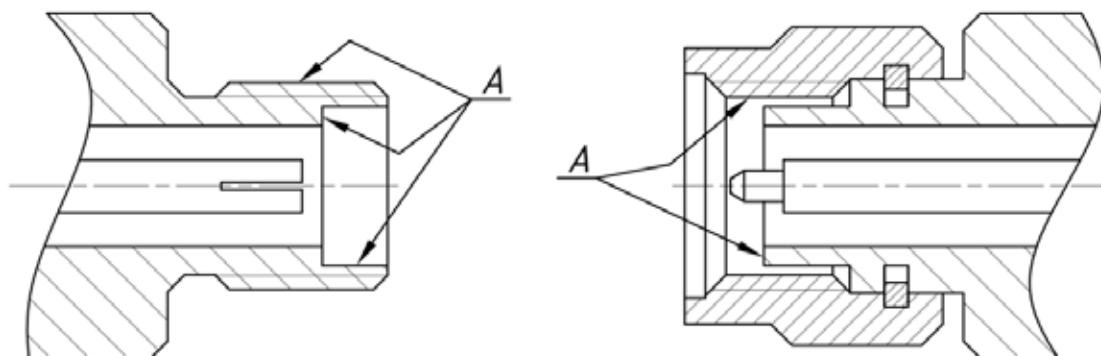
Чистка изделий на примере соединителя типа IX, вар. 3
